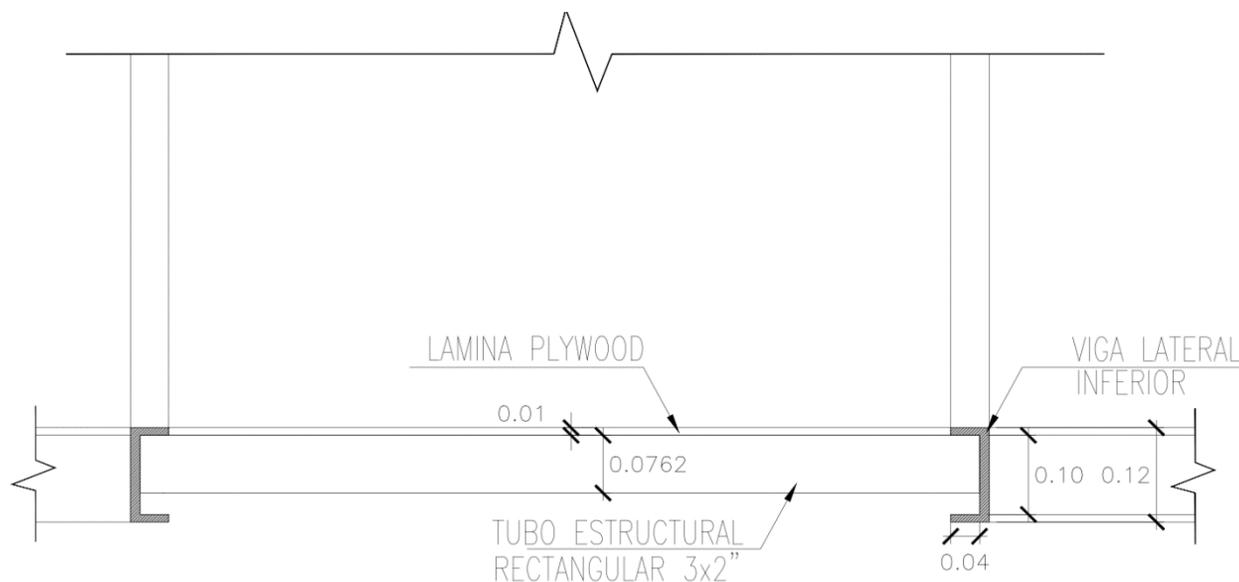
Detalle Soldadura unión entre el Refuerzo y la Viga Lateral Inferior.
